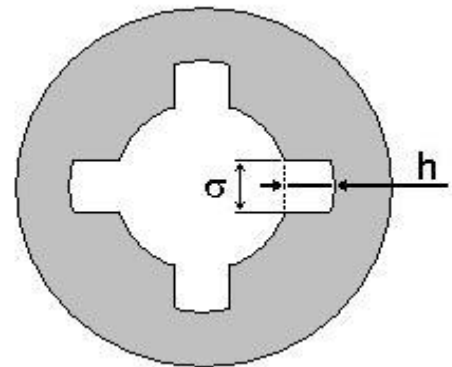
Базовый цилиндр со шлицевыми пазами
